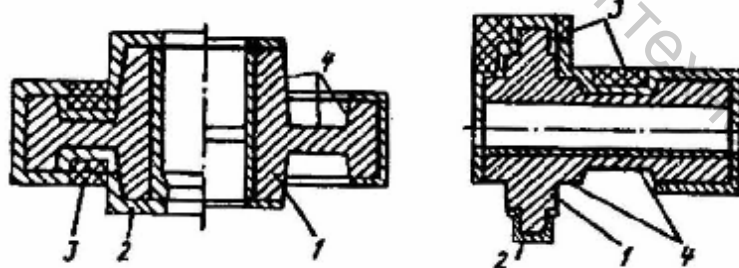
Соответствие формы детали и заготовки, полученной свободной ковкой и штамповкой в открытом штампе и на ГКМ
